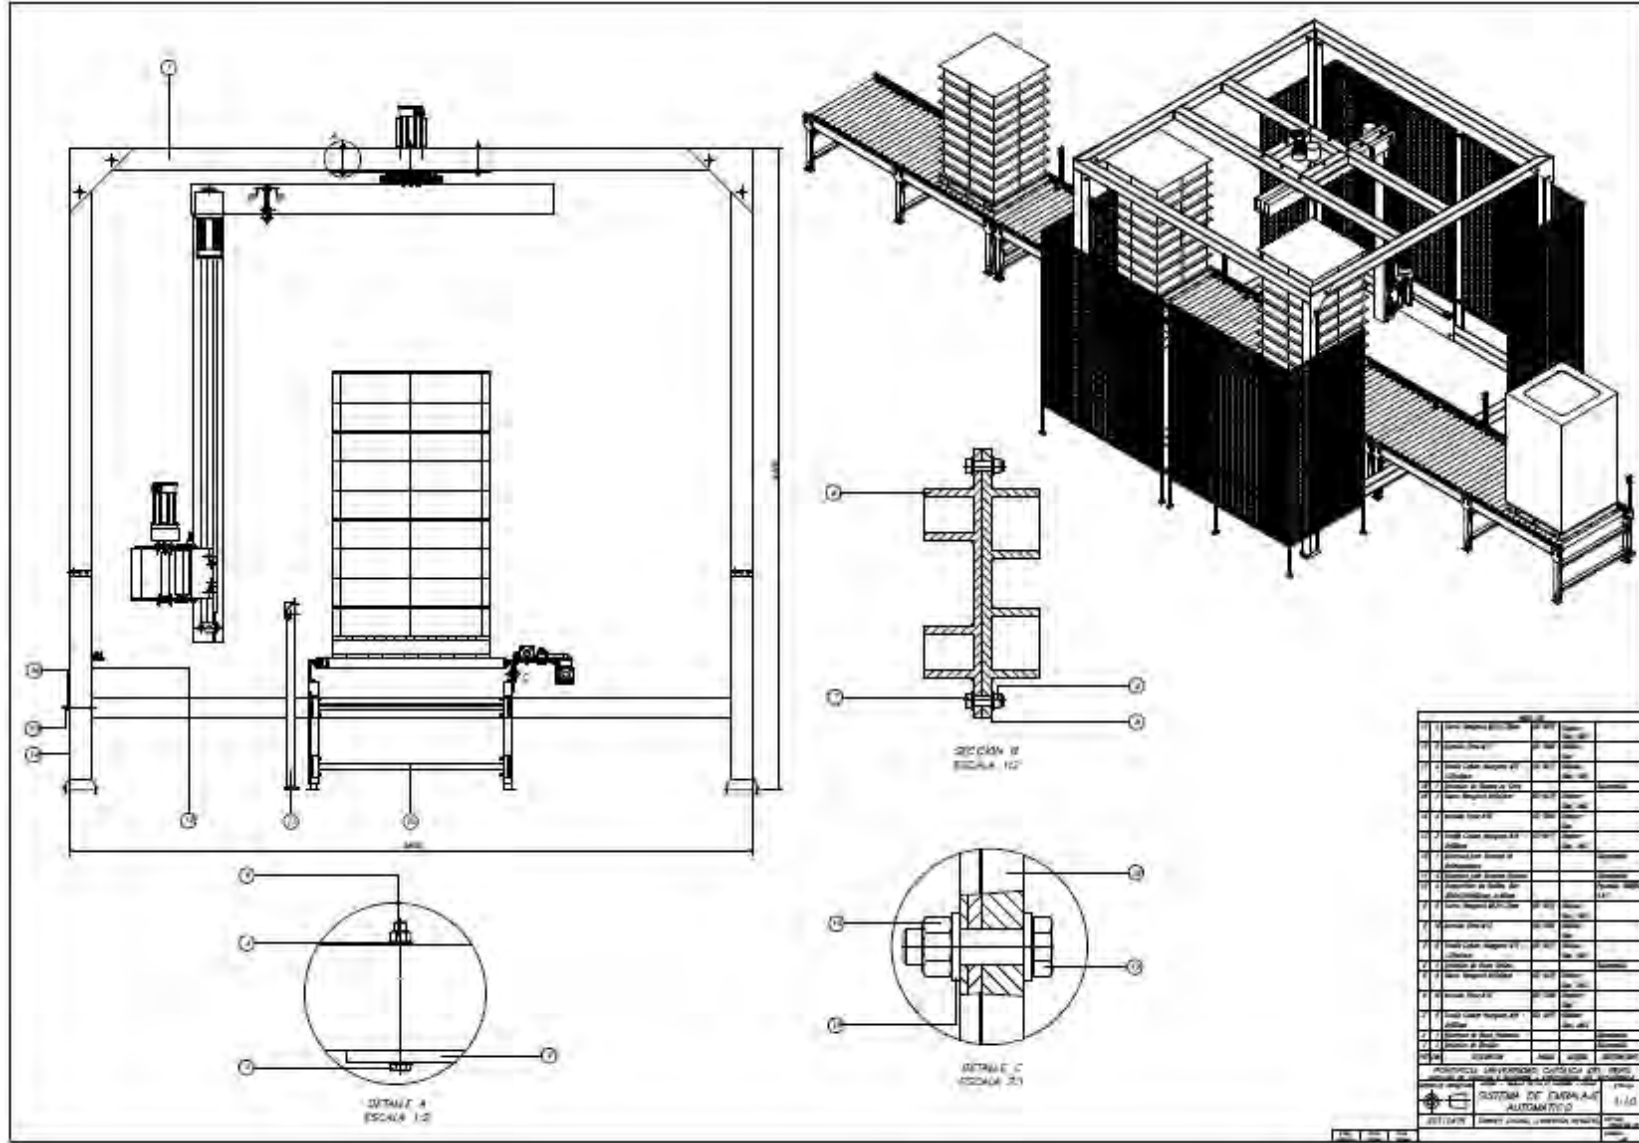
Sistema de Embalaje. Plano. Fuente: Propia.
